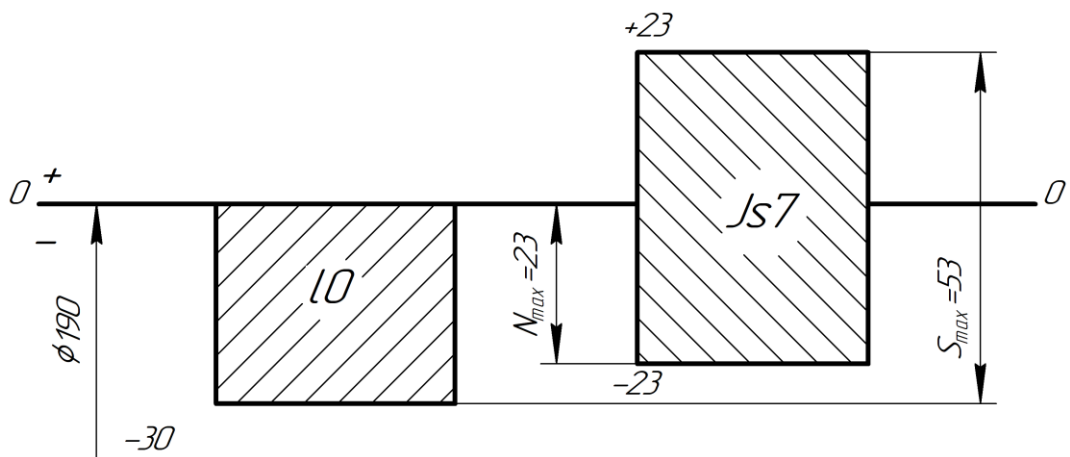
Схема полей допусков сопряжения «наружное кольцо – отверстие в корпусе»
